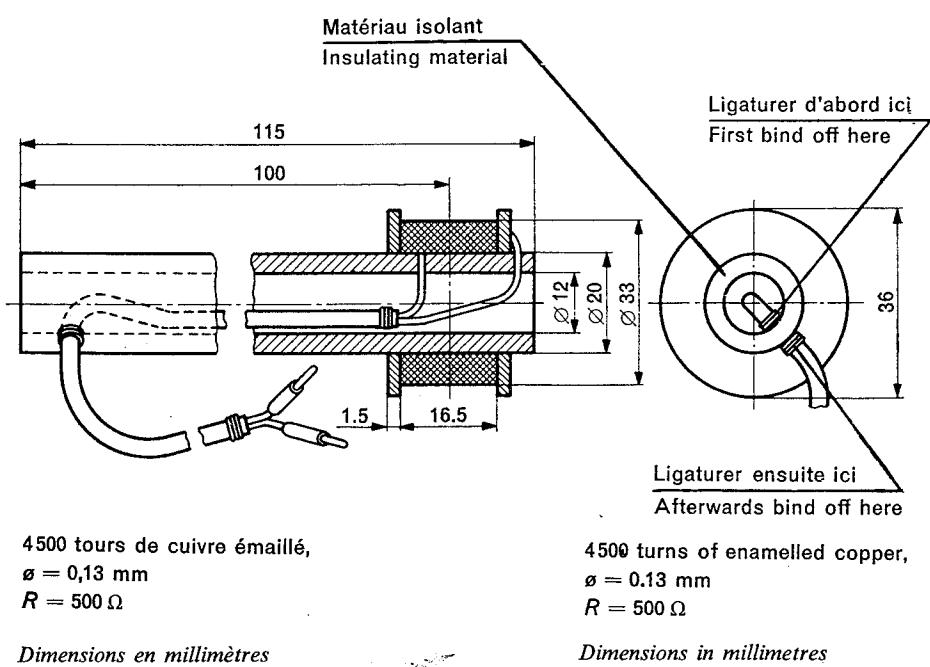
Bobine exploratrice pour la mesure de l'intensité des champs magnétiques.
